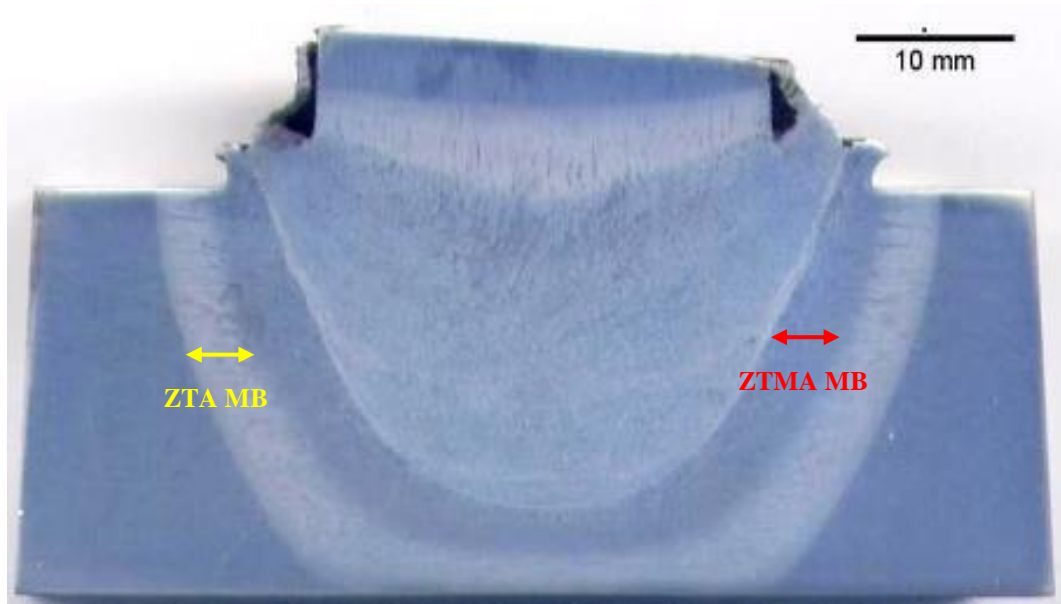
Macrografia da solda F45 na condição de como soldado. Ataque Nital 2%.
